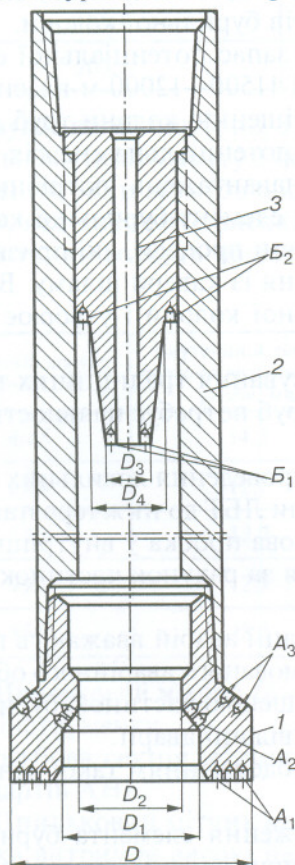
Схема комбінованого пристрою для оббурювання, обробки верхньої частини аварійного об'єкта та шаблонування його внутрішнього каналу:
